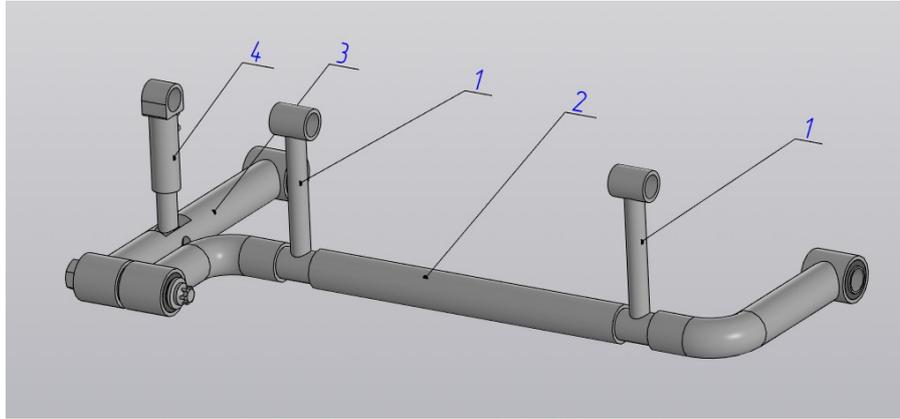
Общий вид стабилизатора с гидроцилиндром:
